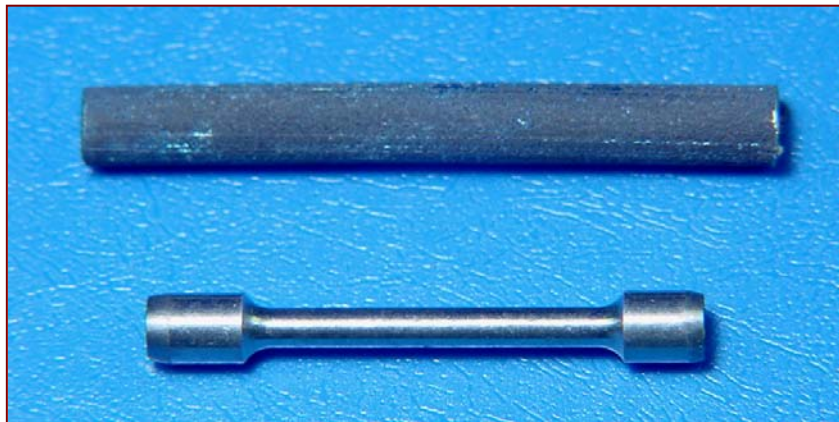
Imagem do cilindro de titânio fundido e corpo-de-prova após usinagem
